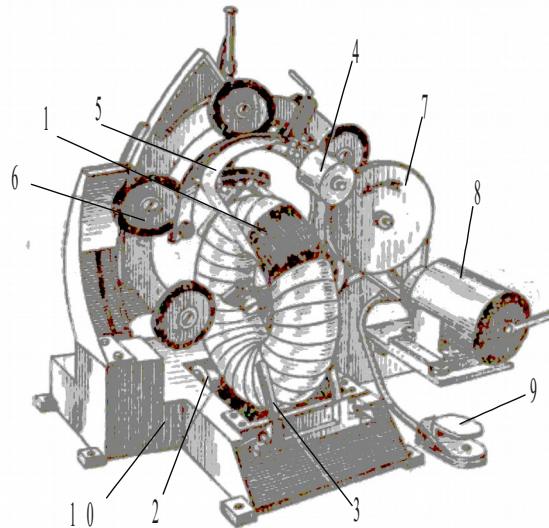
Машина для впакування дроту: 1 - моток дроту; 2 - приводний опорний ролик; 3 - напрямна; 4 - оплеточний рулон; 5 - кільце; 6 - притискної ролик; 7 - обертаючий диск; 8 - двигун; 9 - пускова педаль; 10 - станина
